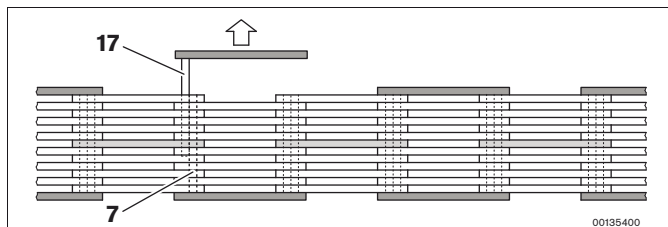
Retirar el muñón con la malla de soldado unida
